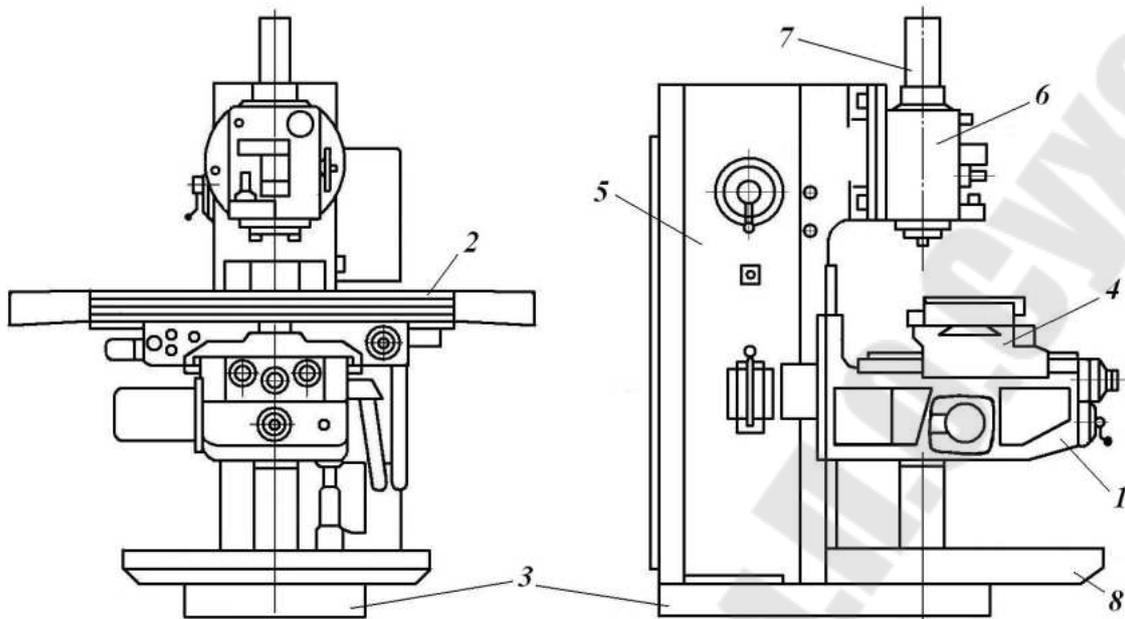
Проекция общего вида вертикально-фрезерного станка FSS350R:
